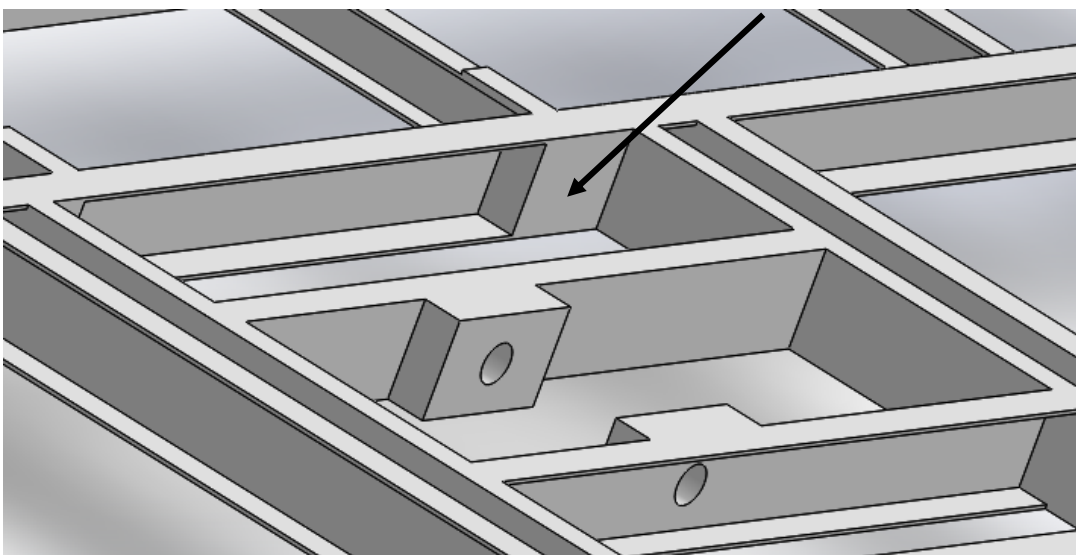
Localización de los refuerzos aplicados en las esquinas inferiores.
